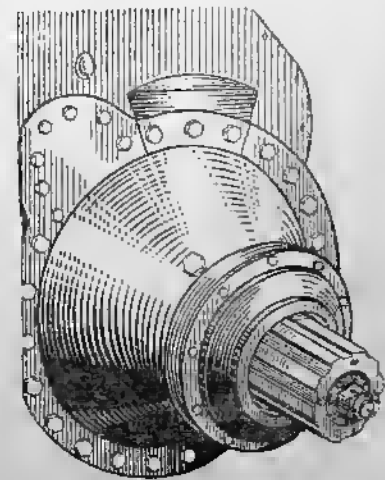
Бортовая передача, установленная на корпусе танка (общий вид)
